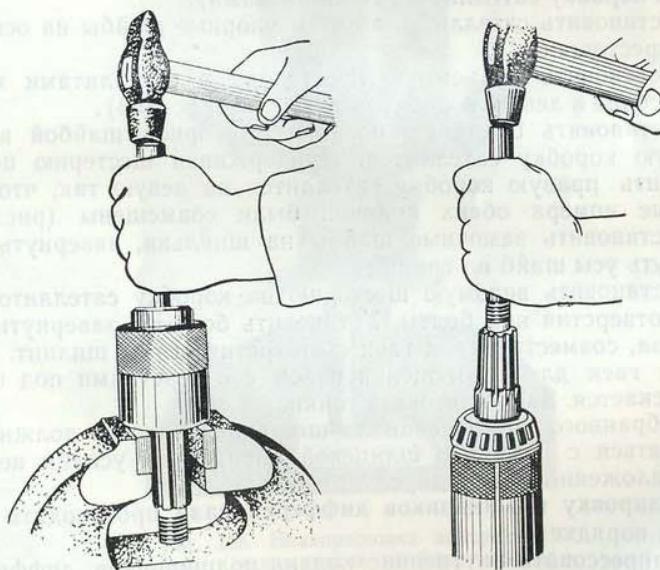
Снятие переднего подшипника с ведущей шестерни
